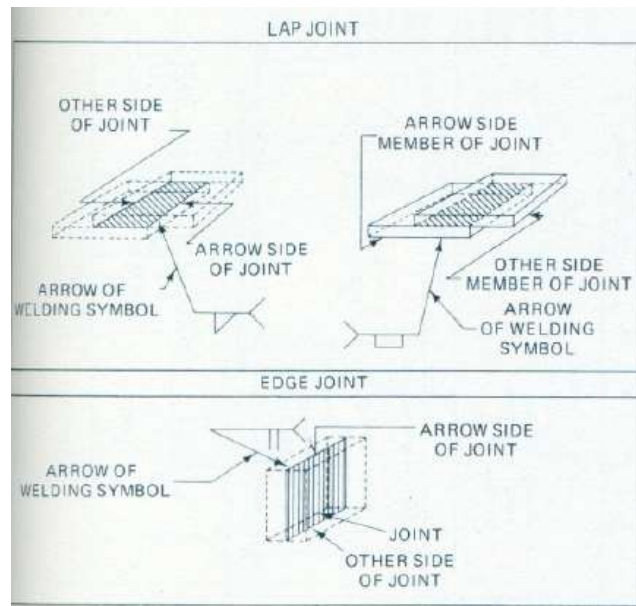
Localización estándar de los elementos de los símbolos de Soldadura (1).
